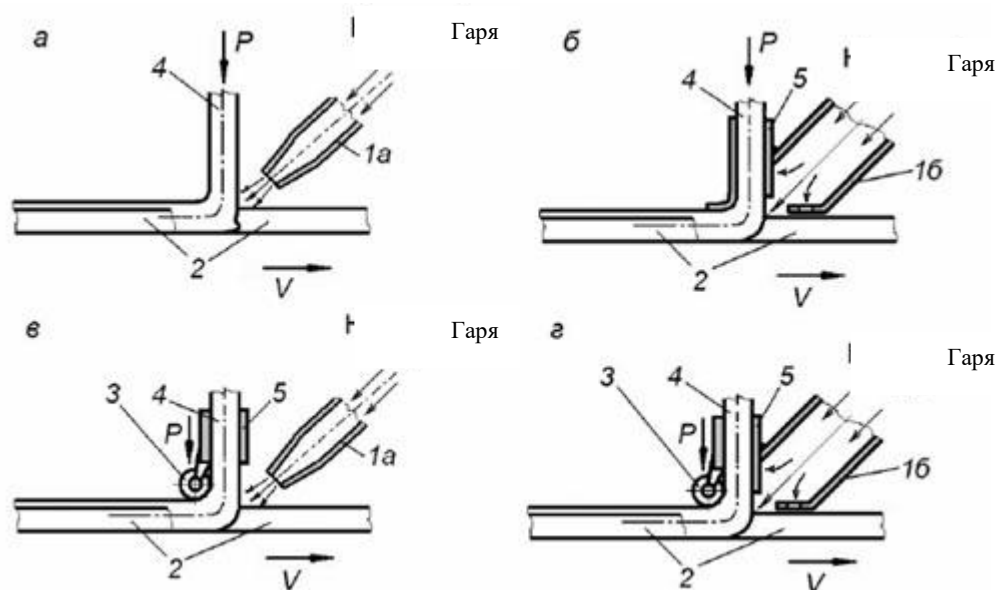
Схеми зварювання пластмас присадним прутком:
